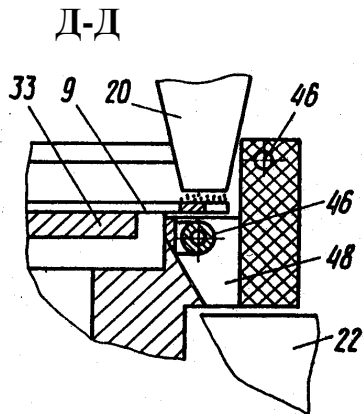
Взаєморозташування деталі і дозатора в індукторі під час засипання шихти на деталь
